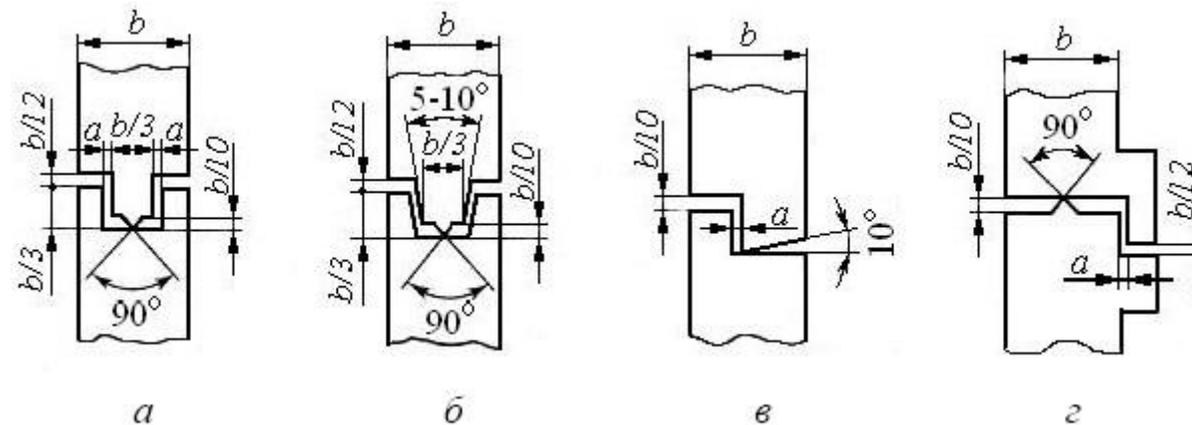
Конструкции кромок стыкуемых деталей при сварке жестких пластмасс ($a = 0,1$ мм)
